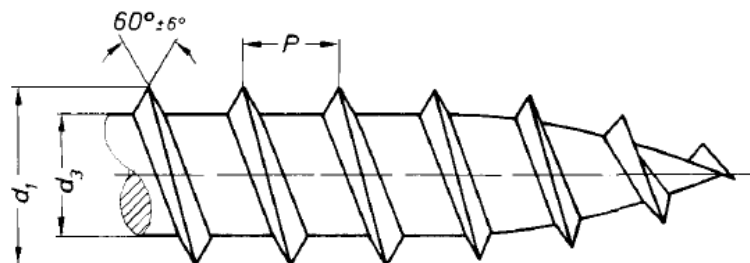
Holzschraubgewinde nach DIN 7998 mit $d_1 = 4$ mm, $d_3 = 2,8$ mm, $P = 1,35$ mm
